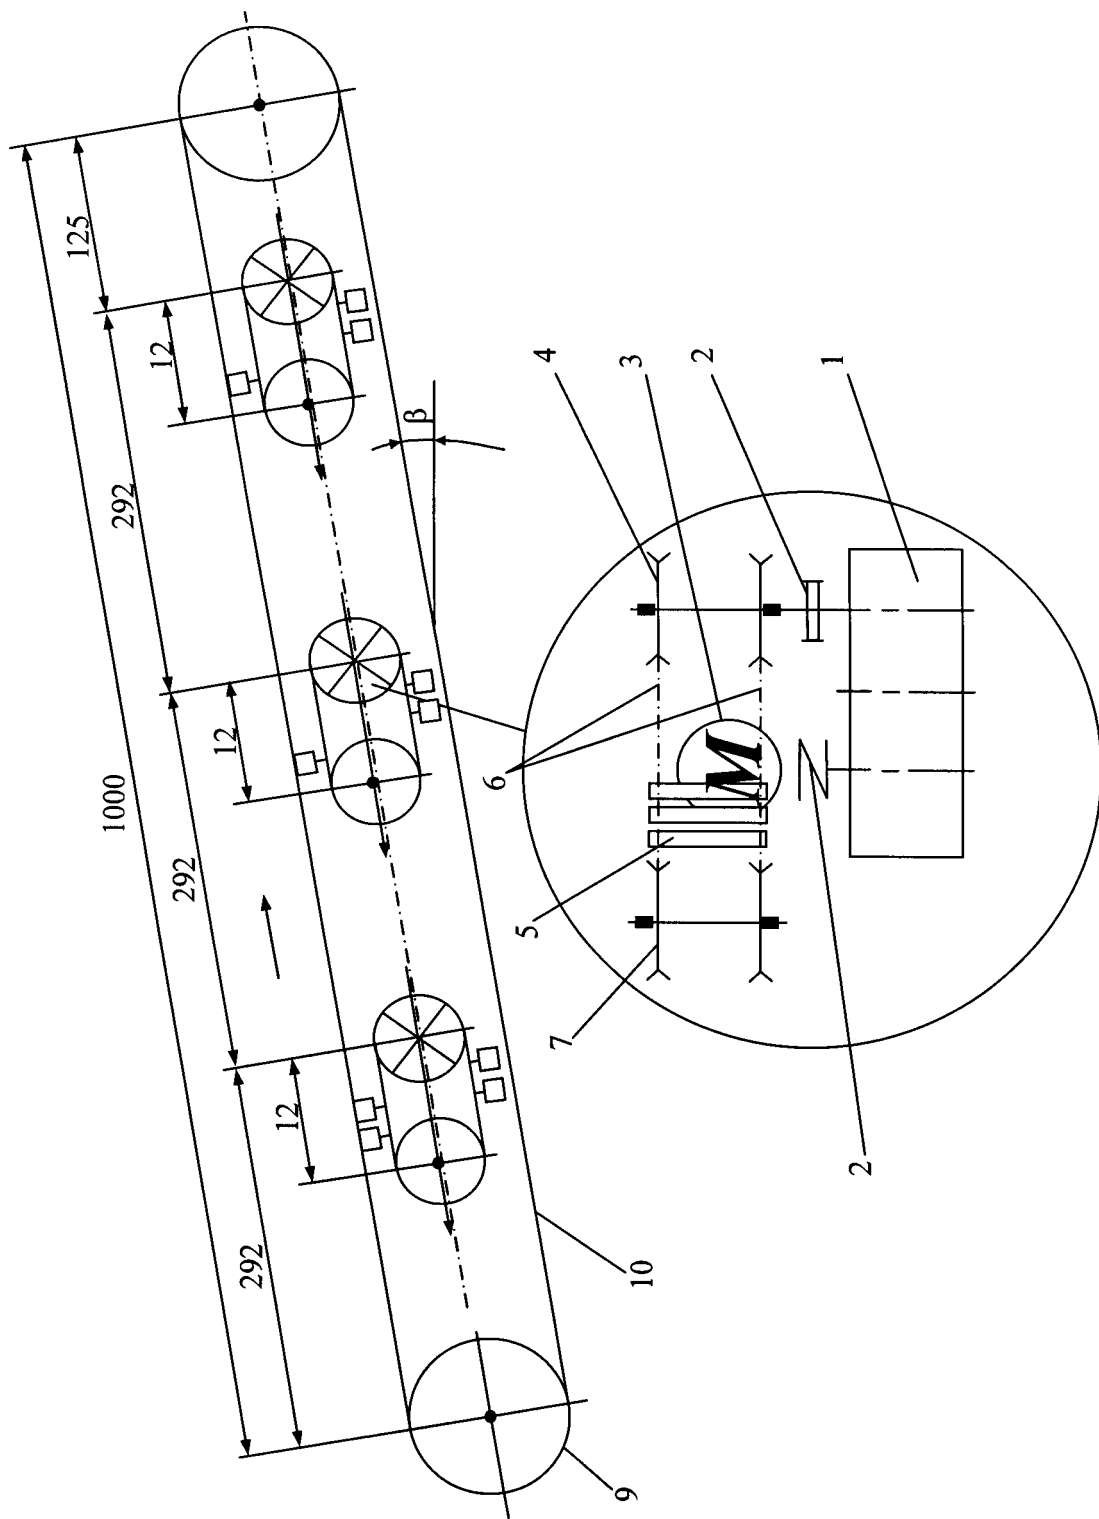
Кинематическая схема магнитно-ленточного конвейера: 1 – редуктор; 2 – муфты; 3 – электродвигатель; 4 – звездочки приводные; 5 – магнитные блоки; 6 – тяговые цепи; 7 – звездочки натяжные; 8 – барабан разгрузочный; 9 – барабан натяжной; 10 – магнитно-мягкая лента
